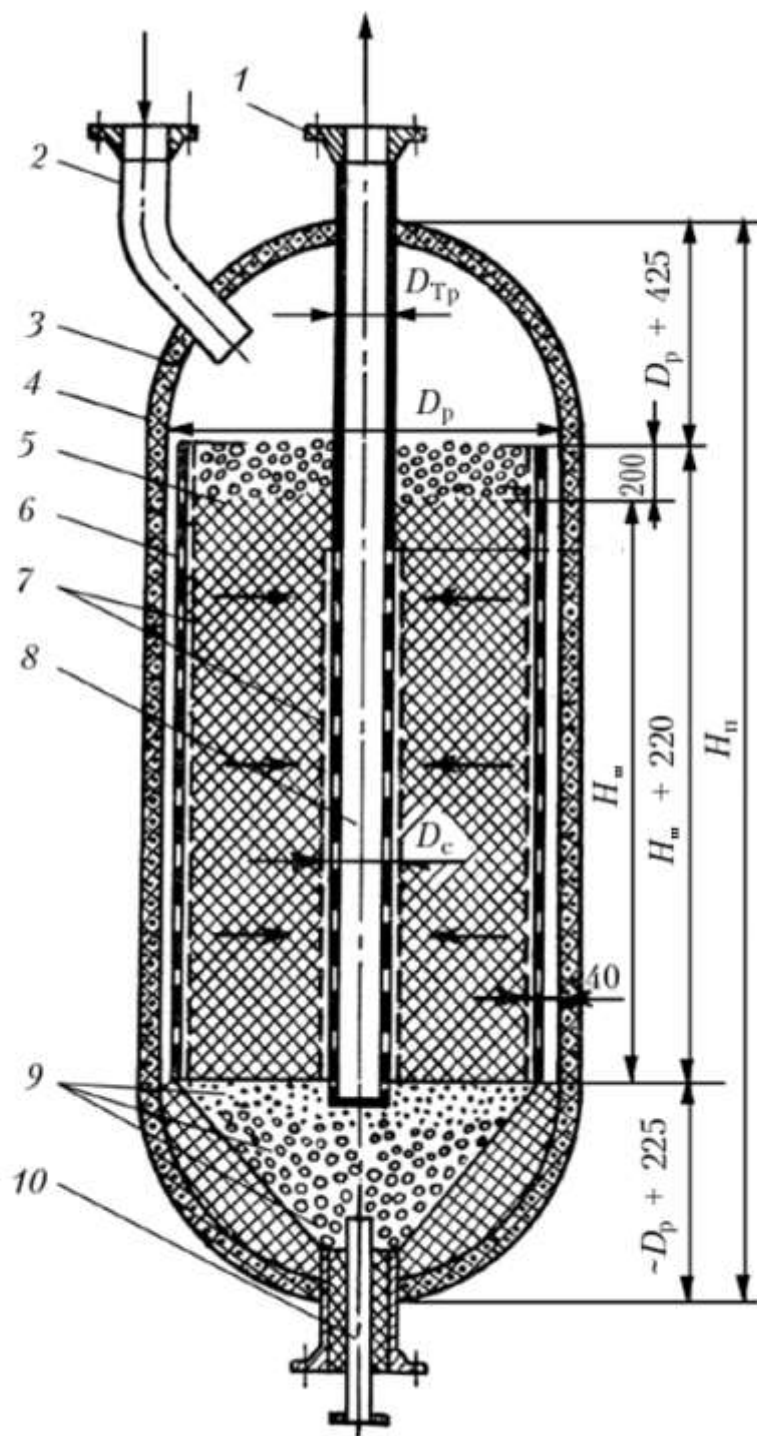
Схема до розрахунку основних розмірів реактора: 1- штуцер для виходу продуктів реакції; 2 - штуцер для входу сировини; 3 – футеровка; 4- корпус; 5 каталізатор; 6 перфорований стакан з сіткою; 7 - сітка; 8 - перфорована труба; 9- кульки порцелянові; 10- штуцер для ежекції газів
